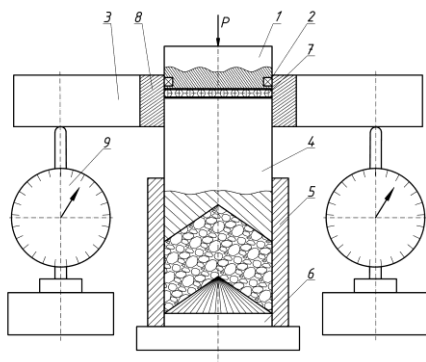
Стендовая установка: 1 – прессующий пуансон; 2 – опорный подшипник; 3 – упор; 4 – подвижный прессующий пуансон с конической рабочей поверхностью; 5 – пресс – матрица; 6 – неподвижный прессующий пуансон; 7 – упорный подшипник; 8 – болтовое соединение, 9- микрометры
